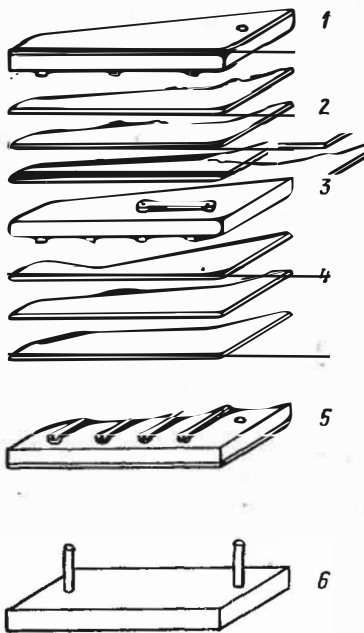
Сборка пакета для прессования многослойной платы:
